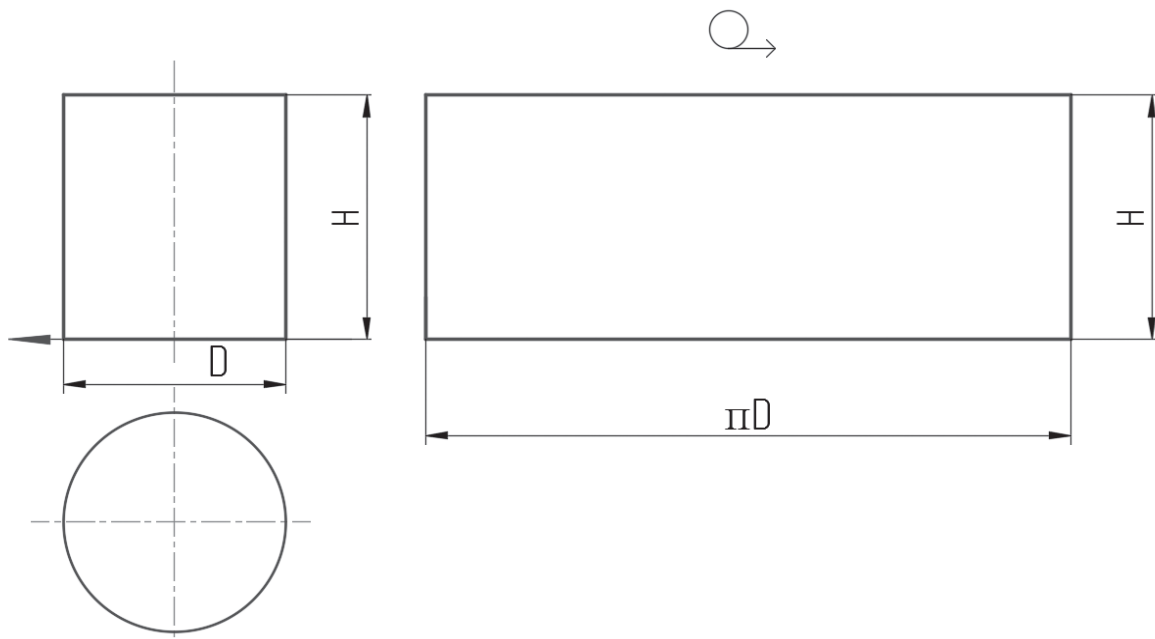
Точная развертка боковой поверхности цилиндра прямого кругового
